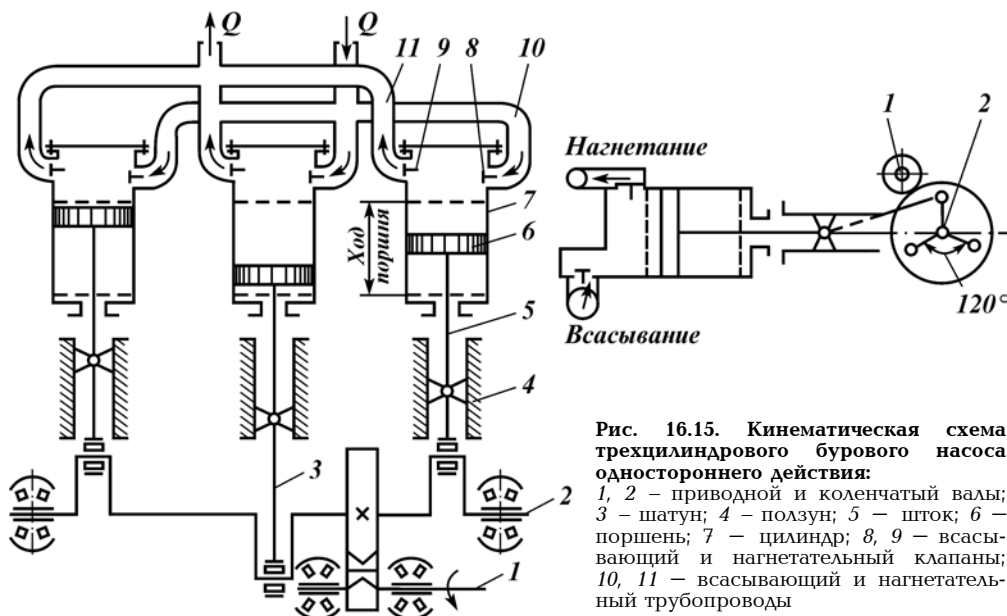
Кинематическая схема трехцилиндрового бурового насоса одностороннего действия: 1, 2 – приводной и коленчатый валы; 3 – шатун; 4 – ползун; 5 – шток; 6 – поршень; 7 – цилиндр; 8, 9 – всасывающий и нагнетательный клапаны; 10, 11 – всасывающий и нагнетательный трубопроводы
